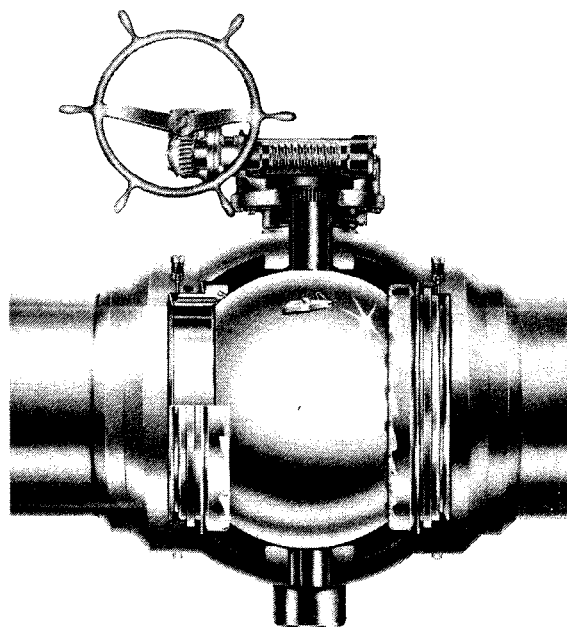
Válvula de bola montada en muñón con asientos giratorios
